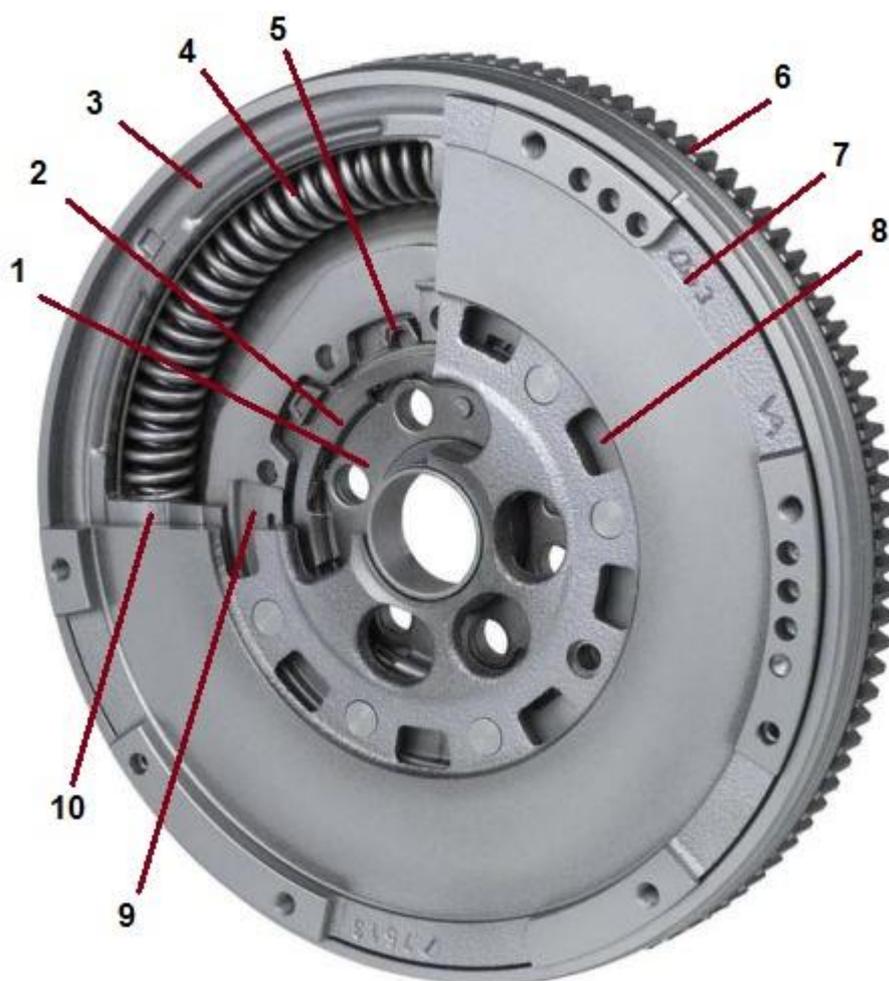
Схема двухмассового маховика: 1- ступица; 2 – радиальный подшипник; 3 – первичный диск; 4 – дуговая пружина; 5 – фланец; 6 –
